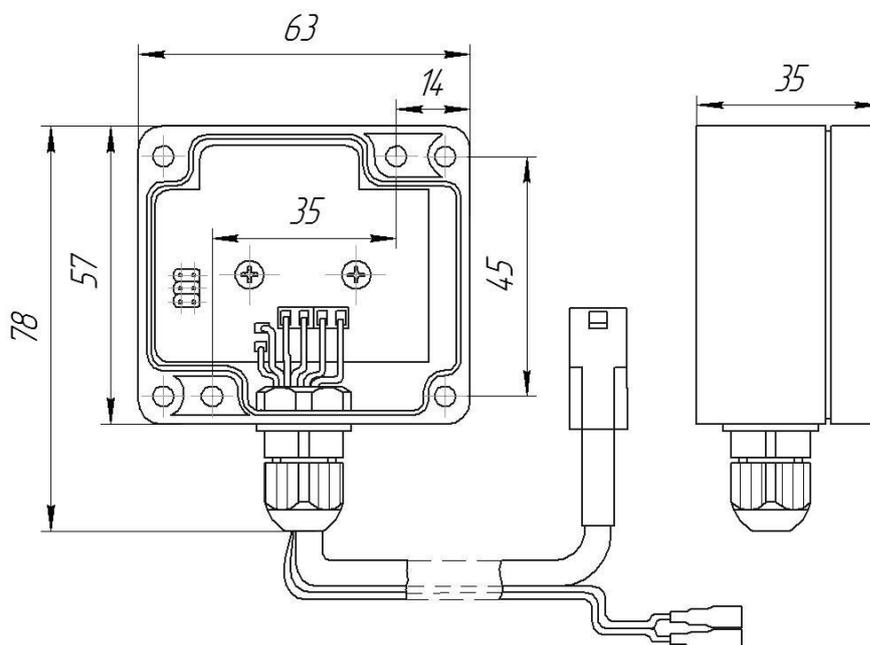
Габаритные и присоединительные размеры ИК-датчика «Луч-М».
